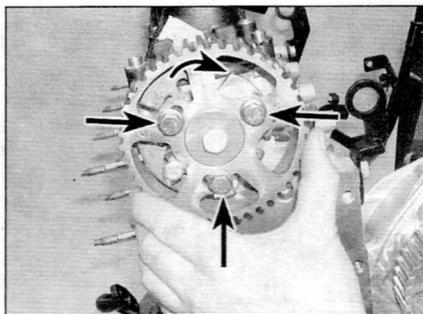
На ранних двигателях отпустите болты (отмечены стрелками) и проверните зубчатый шкив распределительного вала на соответствующей ступице до упора по часовой стрелке (двигатели 2.0 л)
